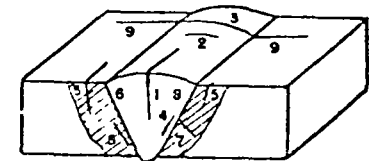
Tipos diversos de grietas en una soldadura a tope.
